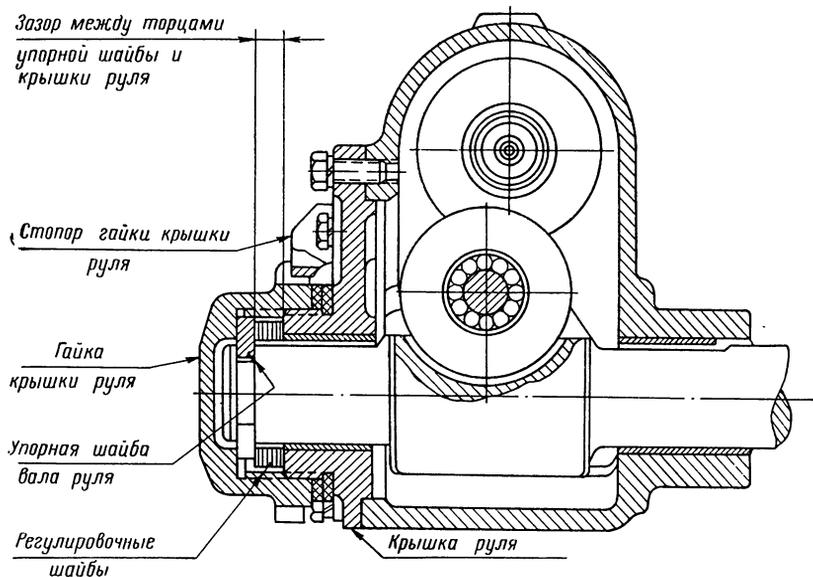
Установка нижней крышки картера, регулировка подшипников и зацепления червячной пары руля
